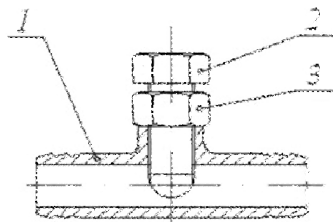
Дозатор газа для инжекторного двигателя:
